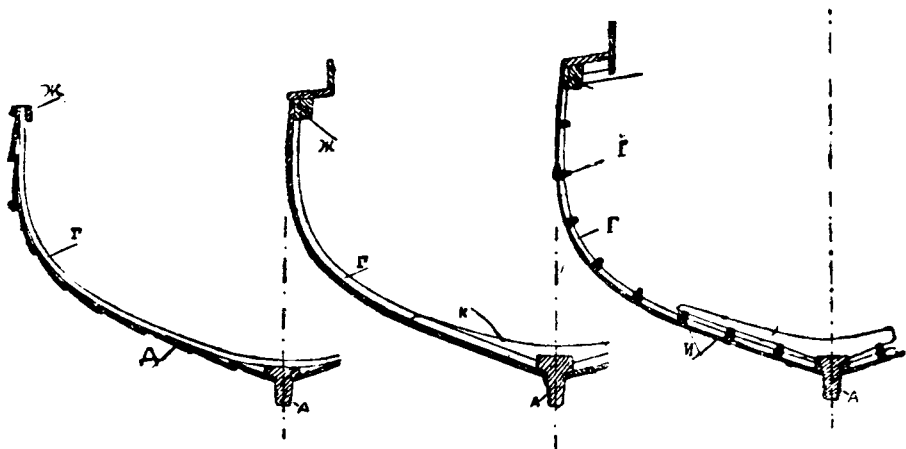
Разрѣзъ строенія корпуса и обшивки трехъ различныхъ системъ. *Лѣвый чертежъ*—обшивка съ наложеніемъ края на край. *Средній чертежъ*—обшивка вгладь двуслойная и потому безъ стыковыхъ брусевъ. *Правый чертежъ*—обшивка вгладь однослойная со стыковыми брусьями, прикрывающими пазы.—*И*, стыковой брусъ—при обшивкѣ борта вгладь.—*И*, стыковые брусья, поддерживающіе полъ. Остальныя буквы объяснены на двухъ предыдущихъ чертежахъ.
